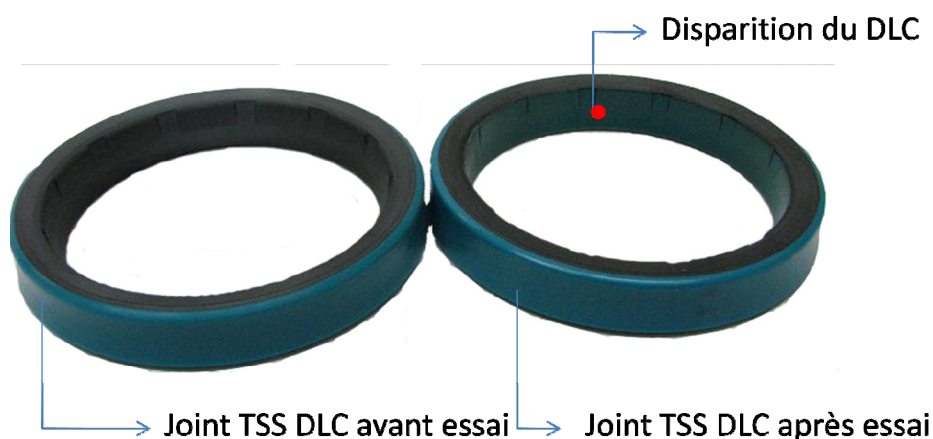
Joint d'étanchéité avant et après l'essai sur banc hydraulique
